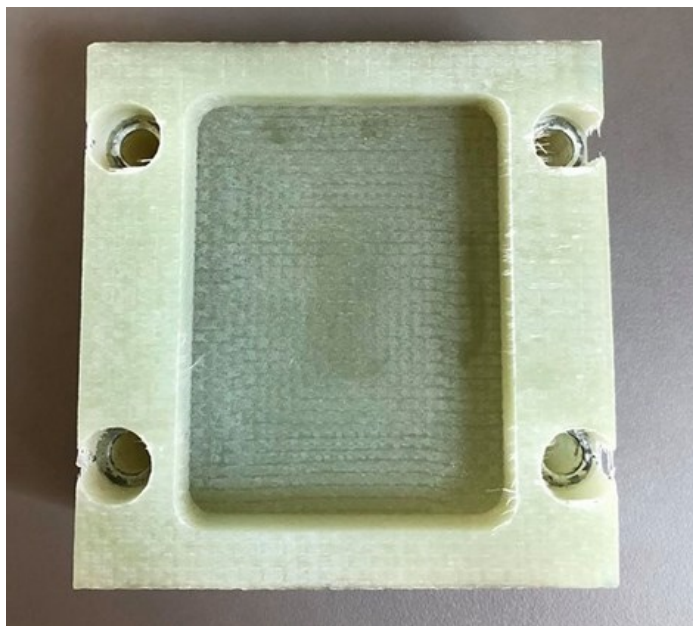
Řezné podmínky a vyznačení obráběného prostoru
